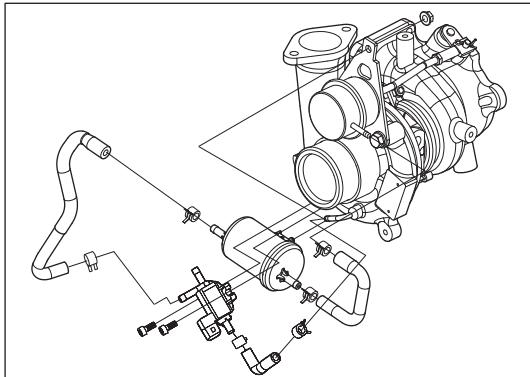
Установка соединительного шланга регулятора давления, соединительного шланга перепускного клапана и клапана регулировки давления турбонагнетателя
